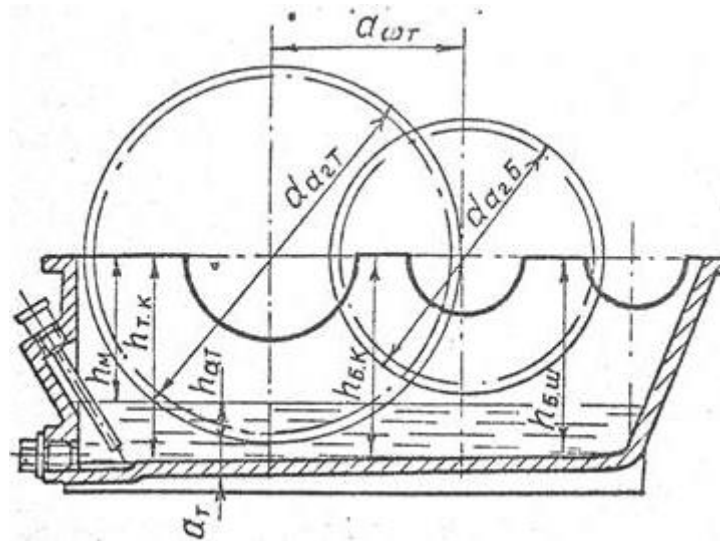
Розміщення зливної пробки і маслоказівника в корпусі редуктора:
